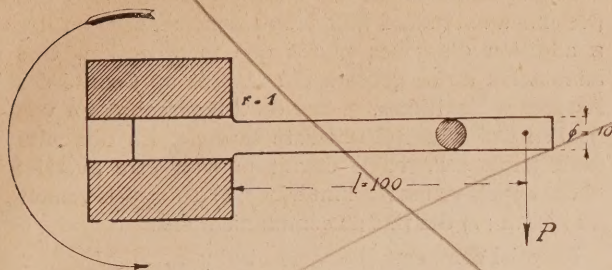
Eprouvette Alpha pour essais d'endurance.
